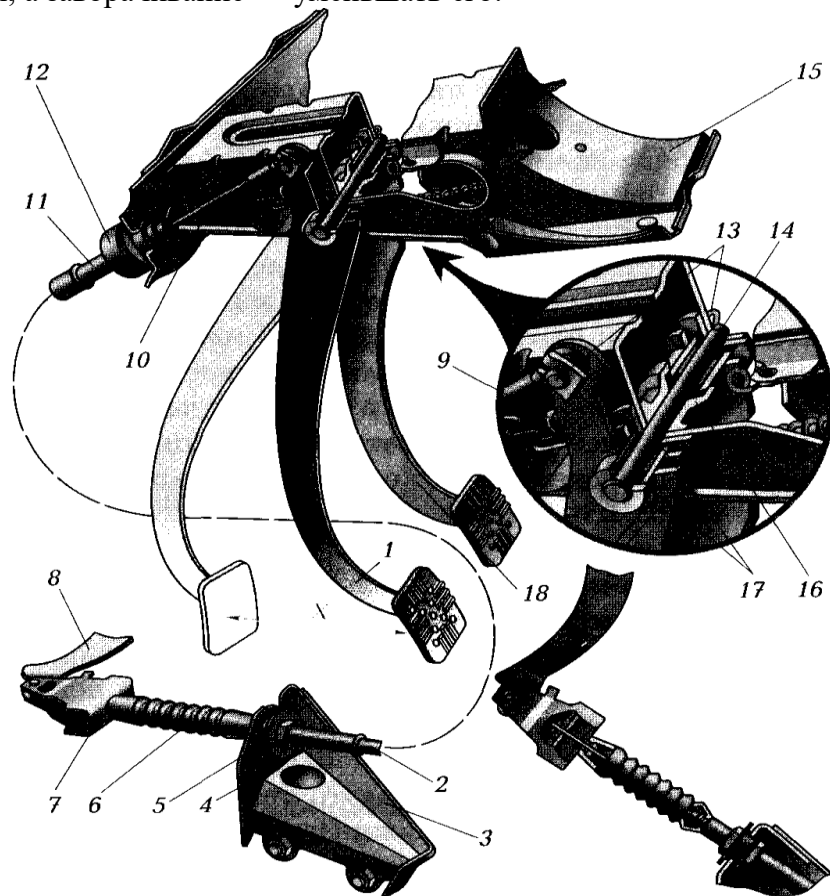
Регулировка сцепления с тросовым приводом: 1 — педаль сцепления; 2 — оболочка троса; 3 — кронштейн крепления нижнего наконечника оболочки троса; 4 — нижний наконечник оболочки троса; 5 — гайка; 6 — защитный чехол; 7 — поводок троса; 8 — рычаг вилки выключения сцепления; 9 — оттяжная пружина педали сцепления; 10 — трос; 11 — верхний наконечник оболочки троса; 12 — обойма; 13 — стопорные скобы; 14 — ось педалей; 15 — кронштейн педалей сцепления и тормоза; 16 — дистанционная втулка; 17 — втулки педали сцепления; 18 — педаль тормоза; X — ход педали сцепления.
